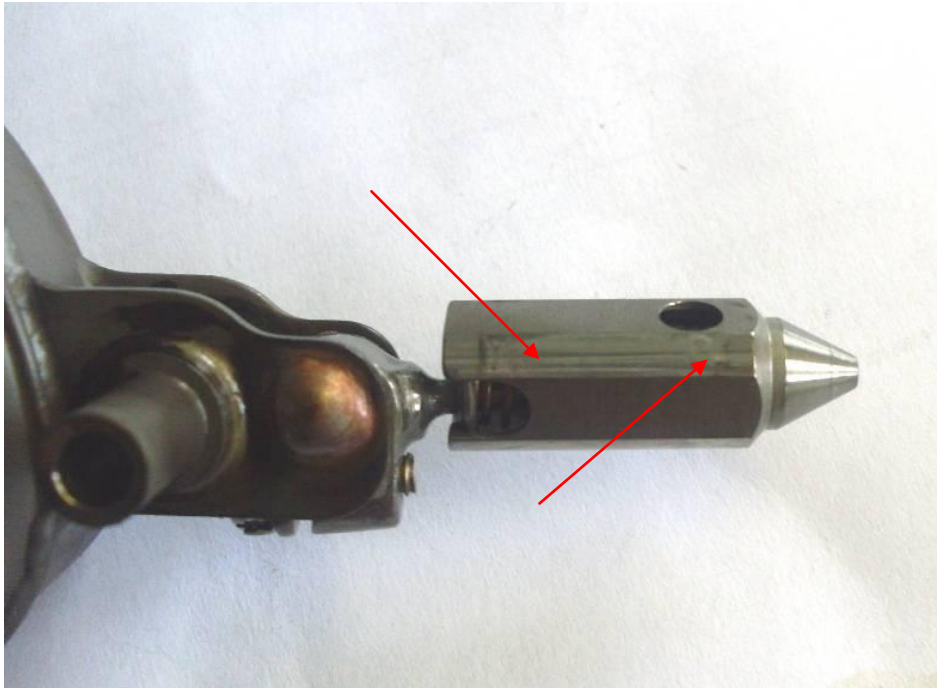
Запорная игла поплавкового механизма с продольными рисками
